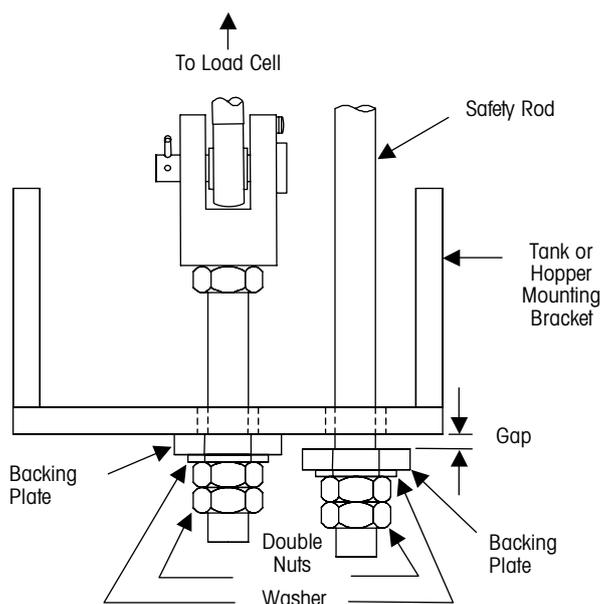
Ensemble du module de pesage fixé au support inférieur
